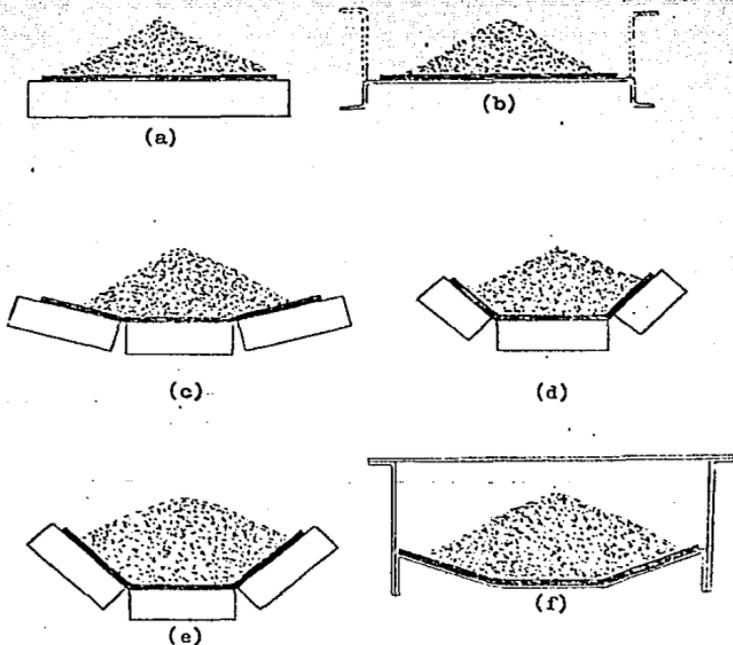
Disposiciones típicas de rodillos intermedios y soportes de placas de transportadores de banda -
